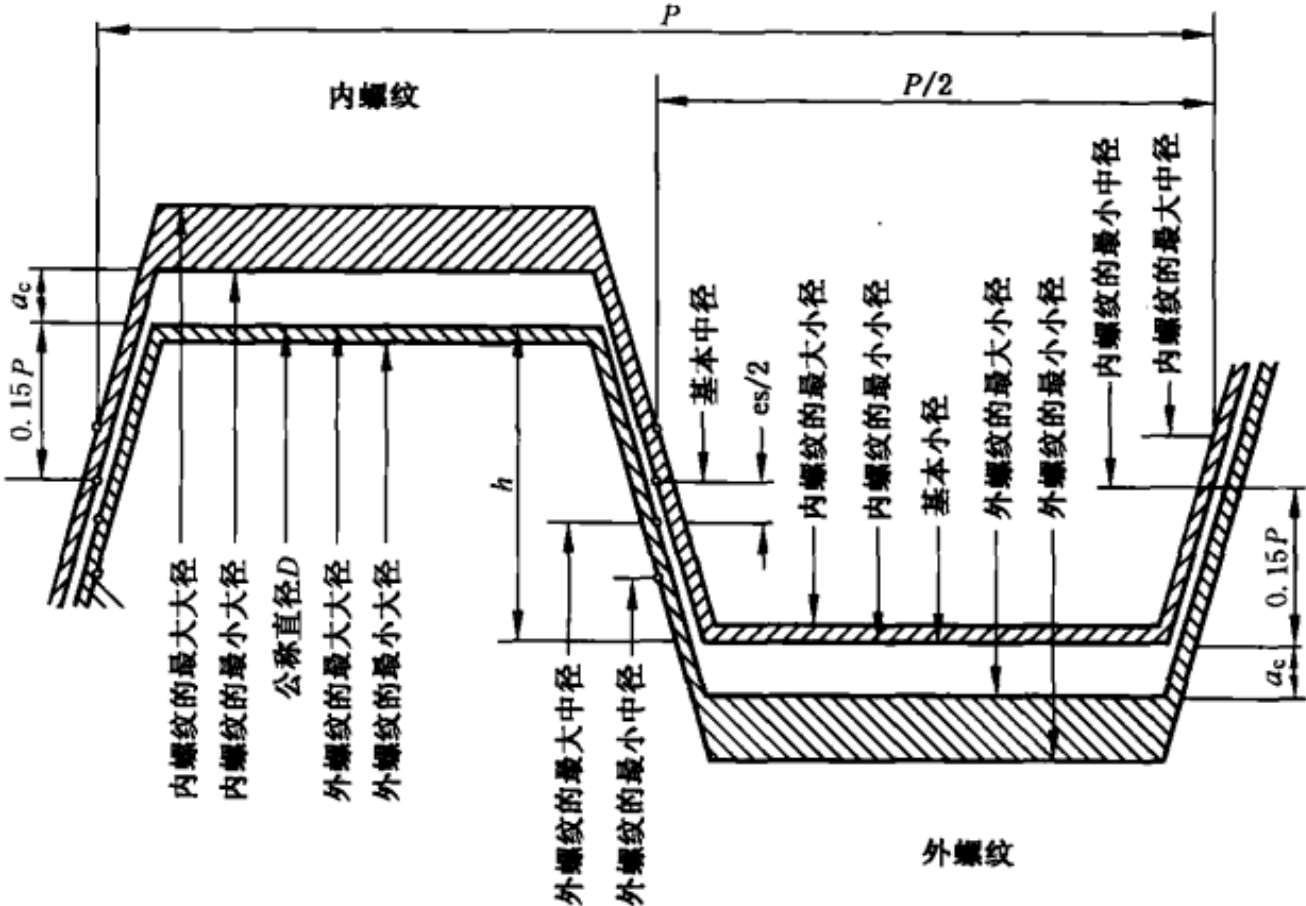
矮牙爱克母螺纹的公差带位置
